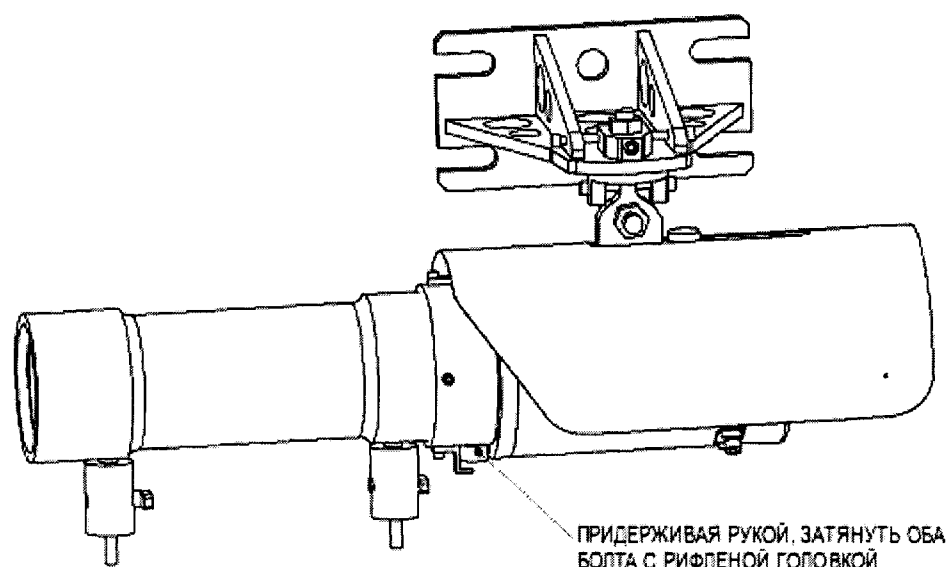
Схема установки кюветы газовой на передней фланец излучателя или приемника
